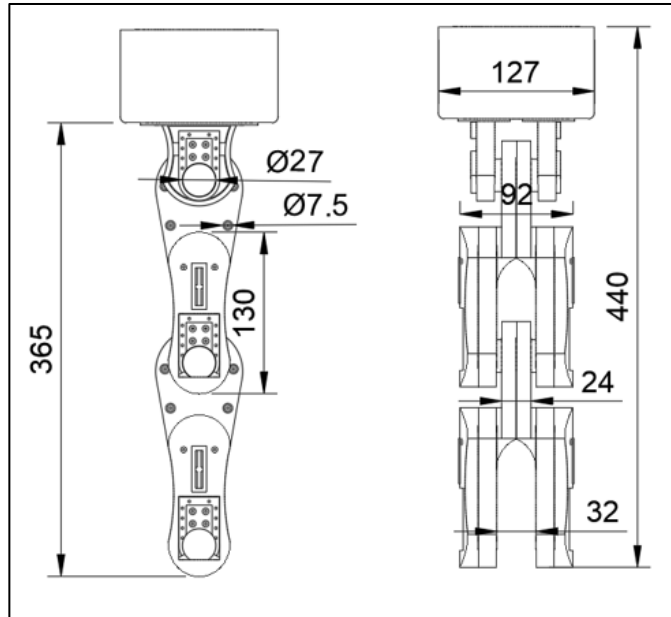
Dimensiones y medidas en mm del brazo. Fuente: Autor
